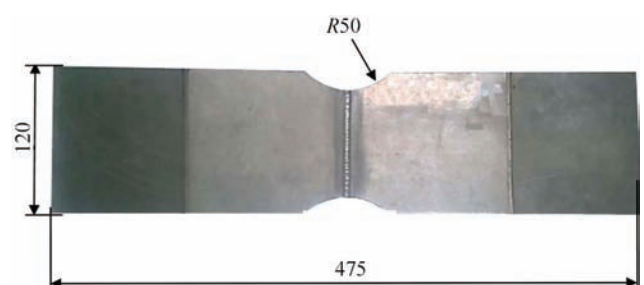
Образец сварного соединения из сплава АМгб для усталостных испытаний
